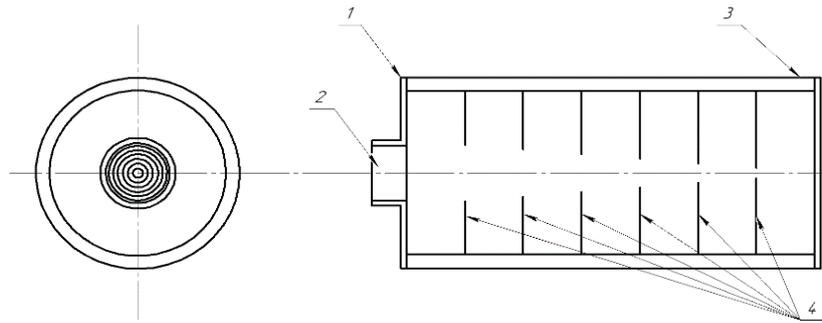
Рассматриваемое газораспределительное устройство: 1 — корпус, 2 — входной патрубок, 3 — блоки, 4 — диски
